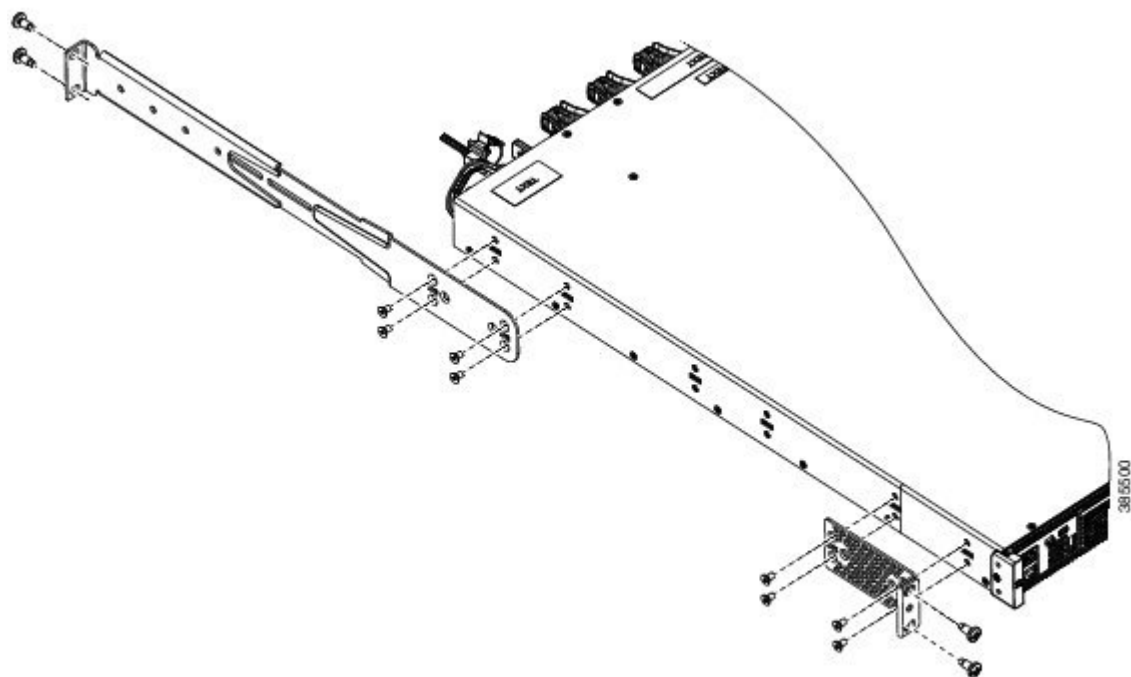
Positions avant, milieu et arrière des supports de montage en rack
